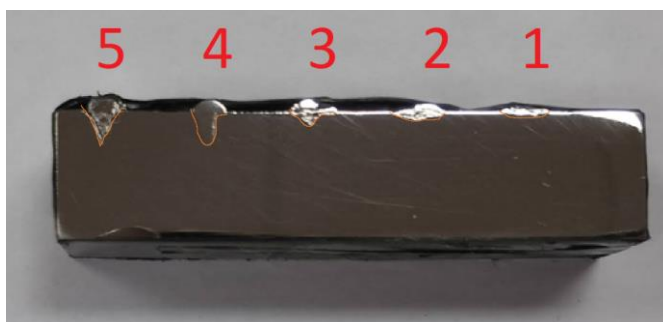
Образец с наплавленными дорожками из проволоки ВТ6, цифрами обозначено количество швов с разными режимами наплавки
